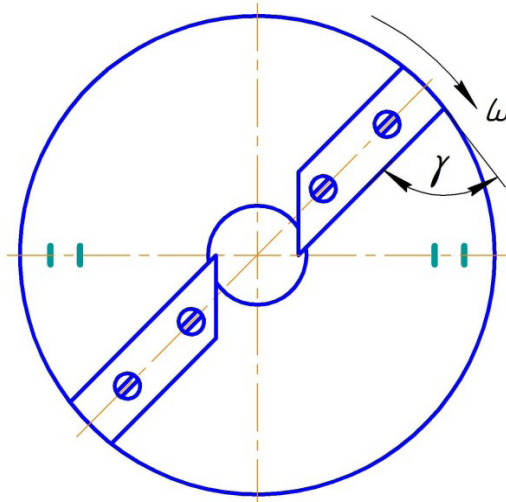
Схема установки горизонтальных ножей на режущем диске
